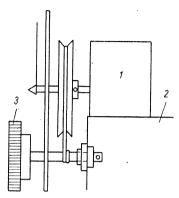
Skalenantrieb für eine Halbkreisskala, bei der der Zeiger auf der Drehkoachse befestigt wurde. 1 — Drehkondensator, 2 — Chassis, 3 — Drehknopf
